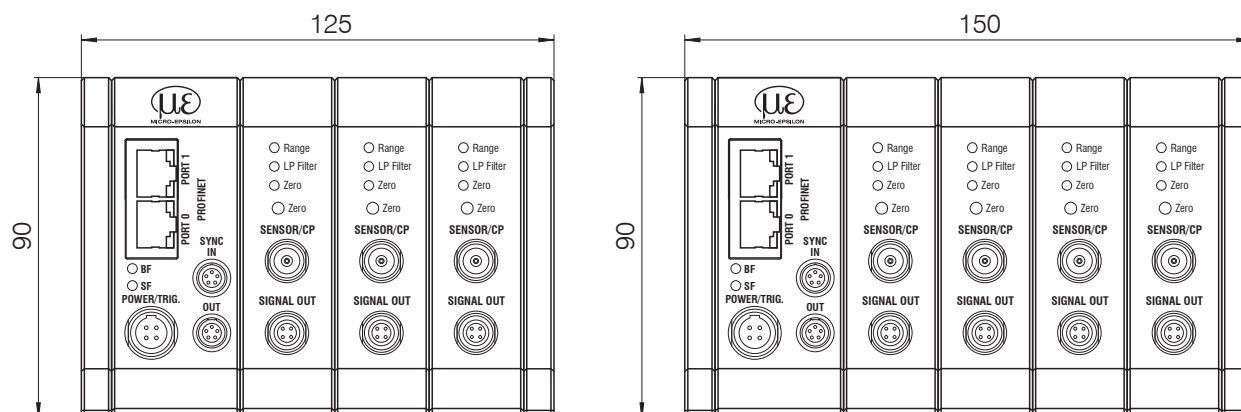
Maßzeichnung Controller mit drei oder vier Demodulatormodulen
